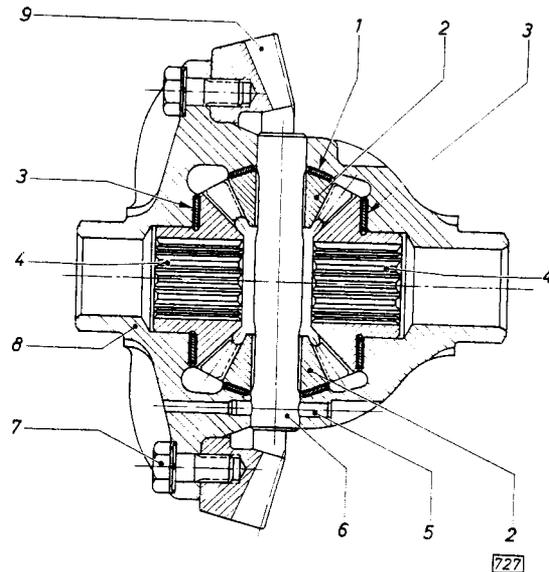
Ausgleichgetriebe mit Ausgleichscheiben für Hinterachswellen- und Ausgleichkegelräder
